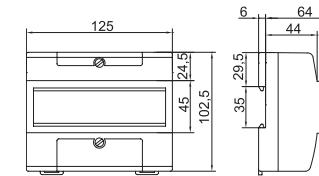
Габаритные и присоединительные размеры счётачиков габарита корпуса 2.
